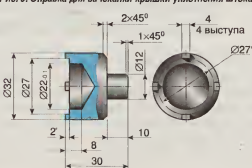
Оправка для выпрессовки крышки уплотнения штока.
